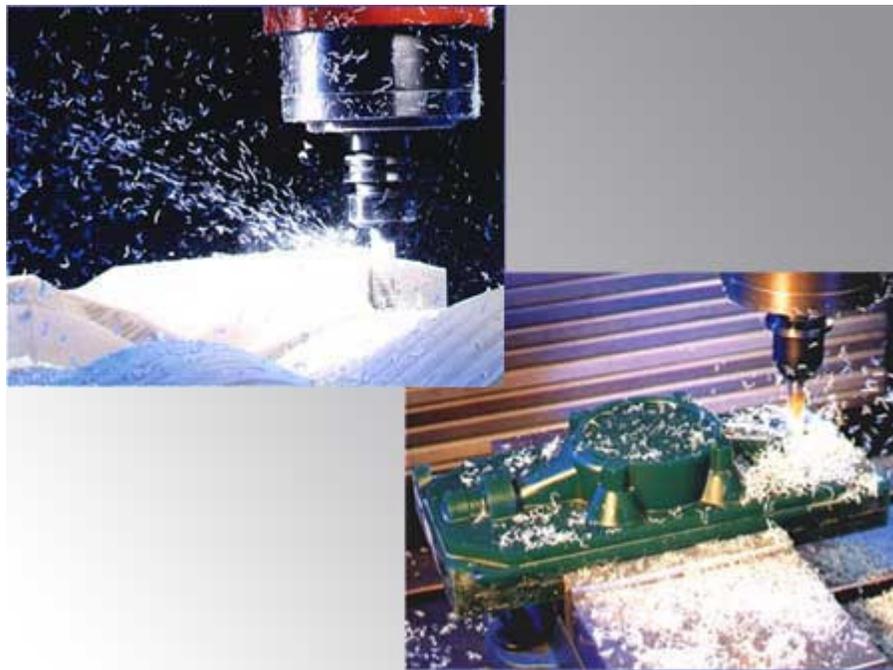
Usinagem de poliuretano em máquina CNC, extraída de VANTICO (17)
